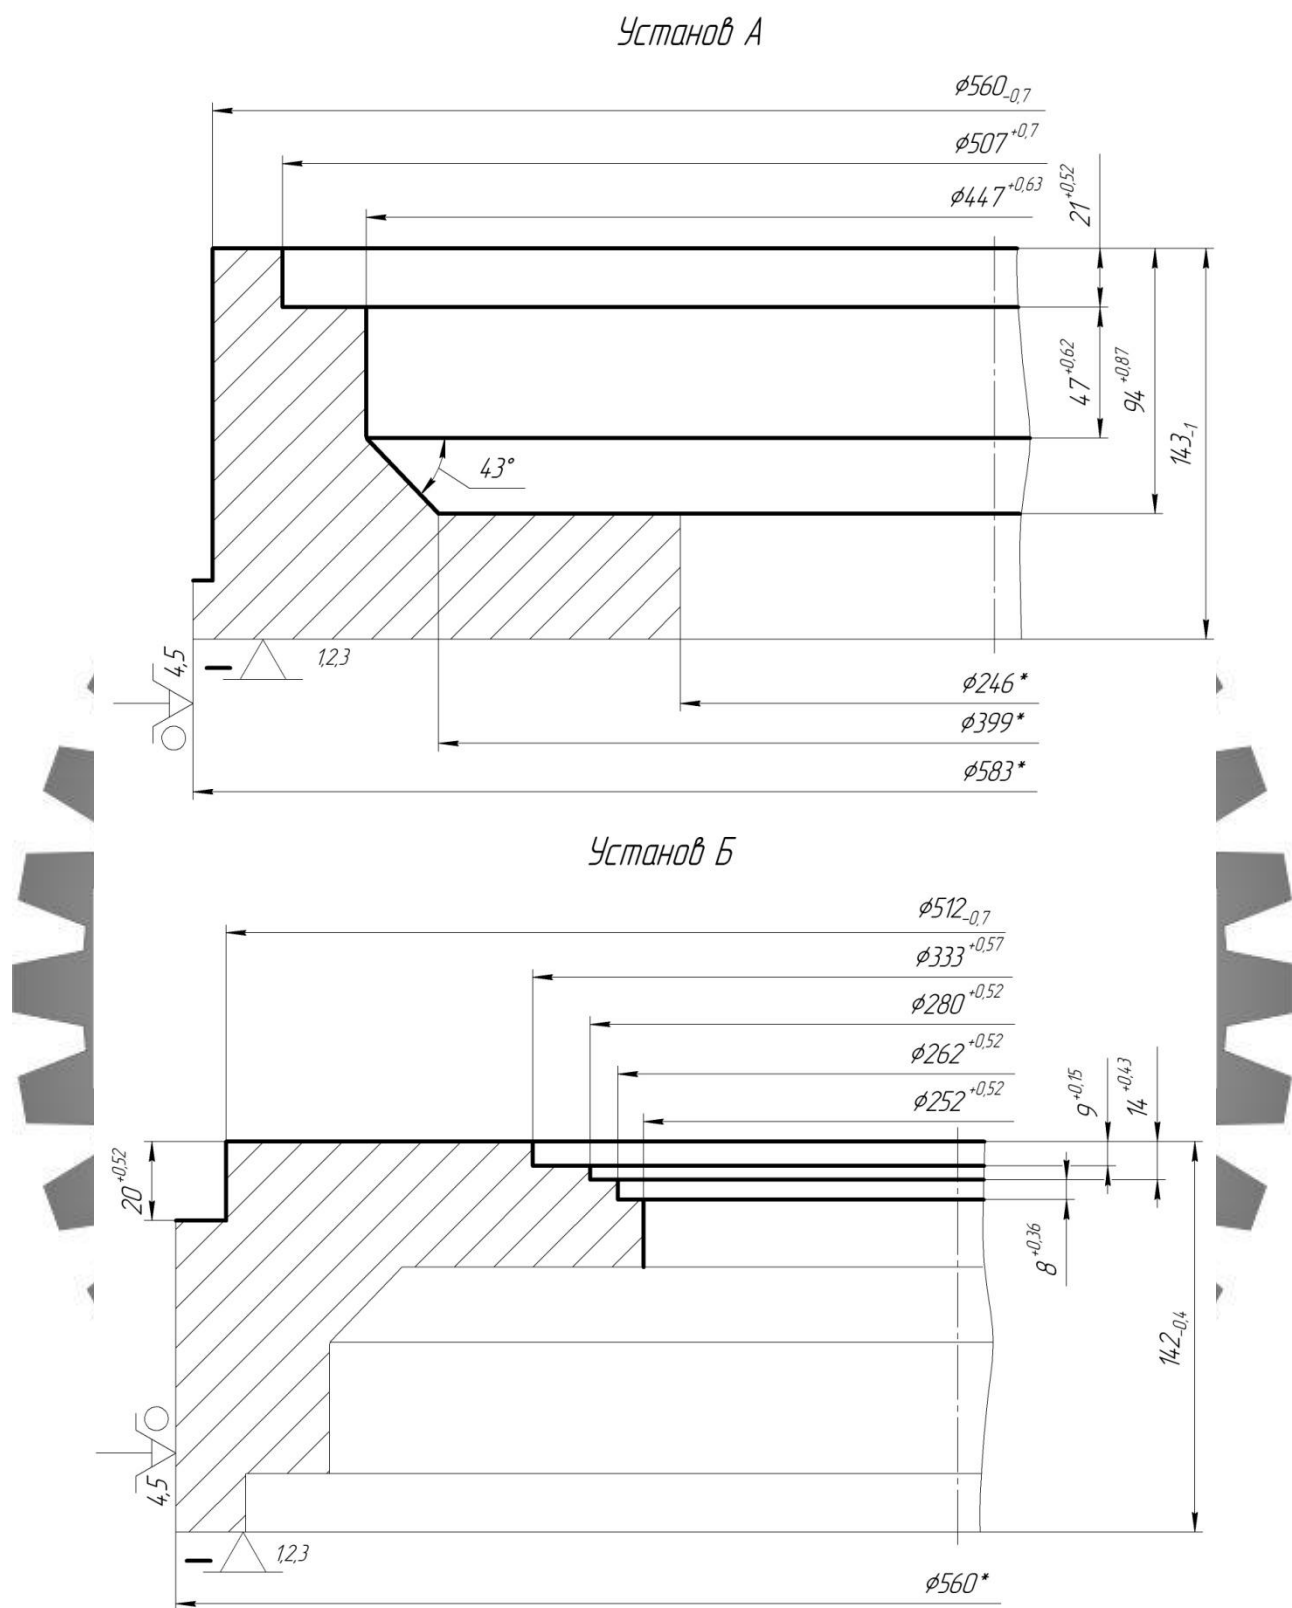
Схема базування заготовки на токарній операції (другий варіант)
